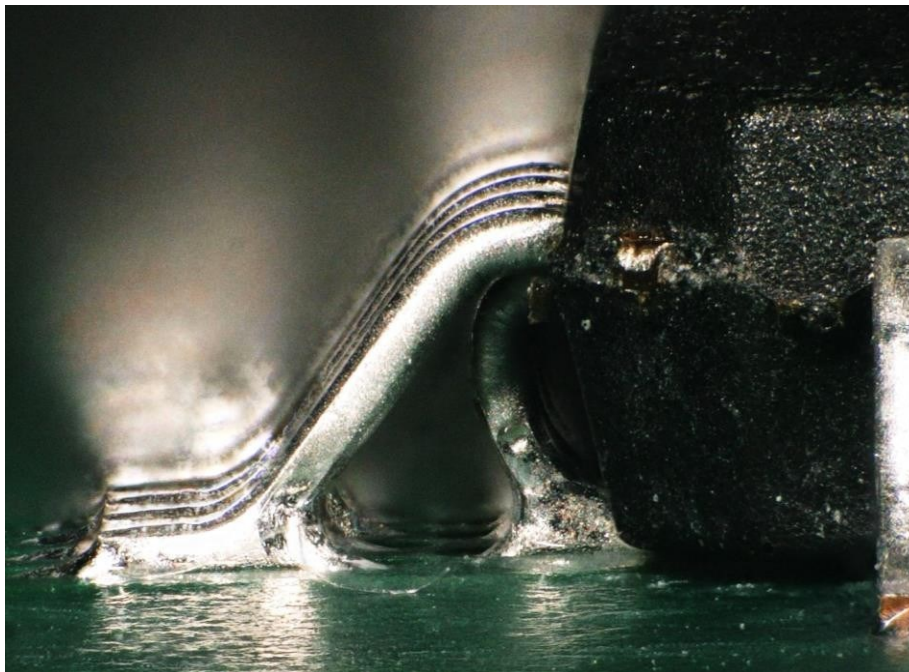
172 MaxQFP 通过回流焊焊接到 PCB 上
